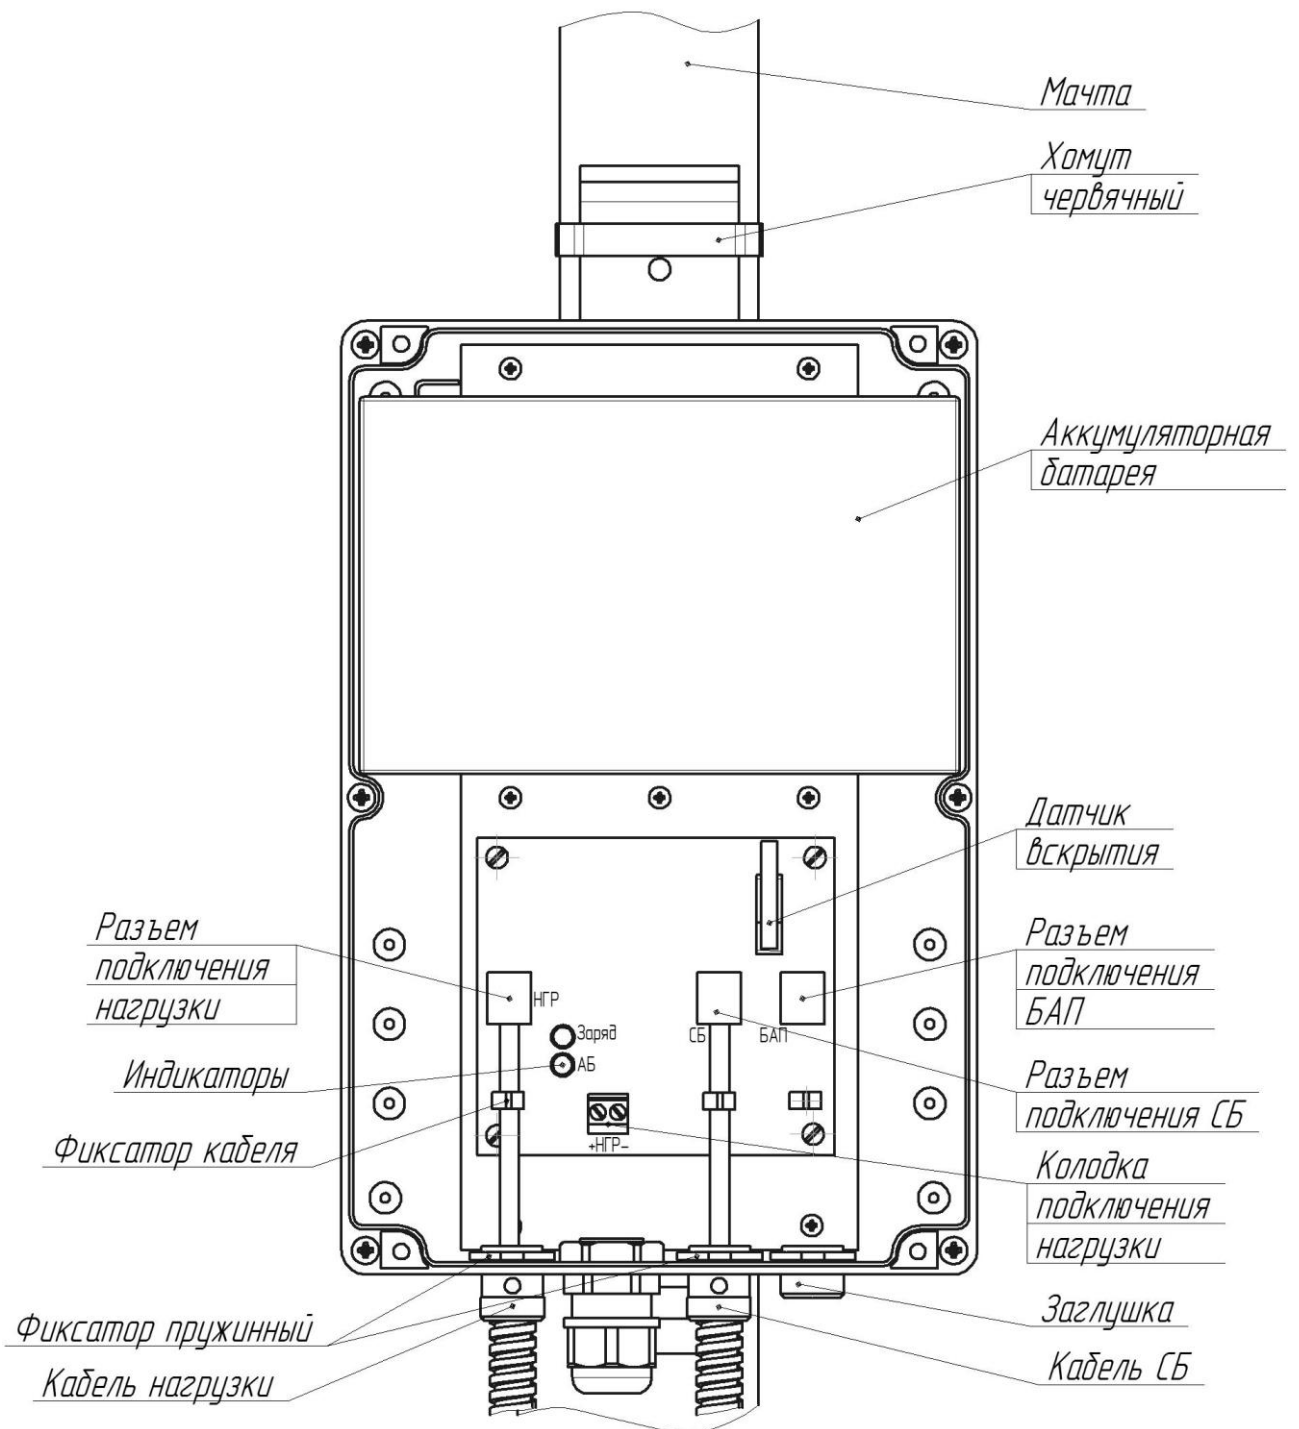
Внешний вид контроллера со снятой крышкой
